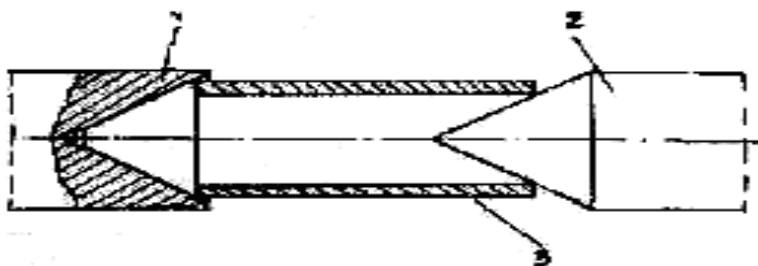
Установка цилиндрической заготовки в центрах
